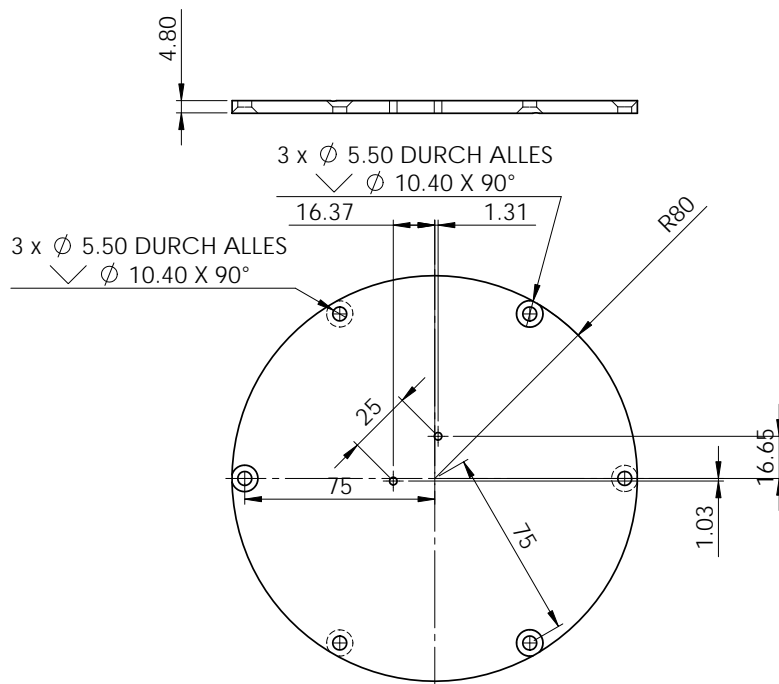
Technische Zeichnung der Bodenplatte.
